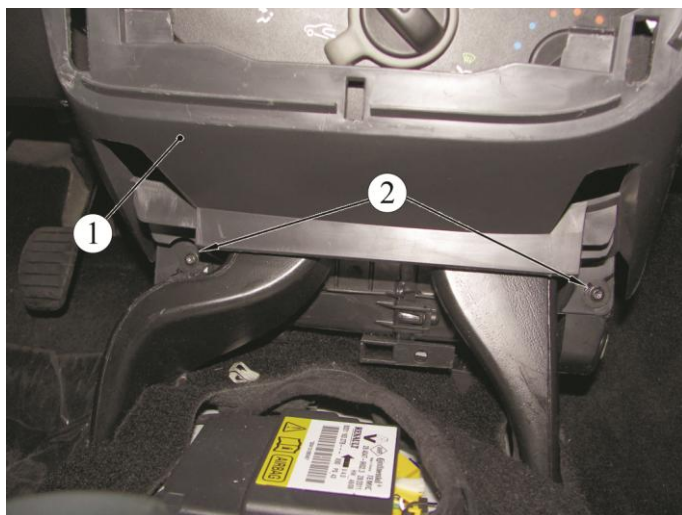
Крепление панели приборов к корпусу отопителя:
